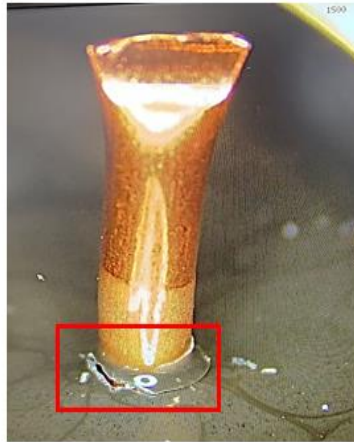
Dispositivo con grietas en el epóxido
